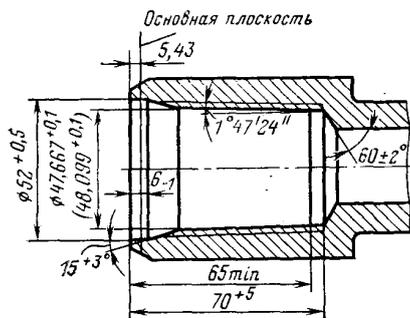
Резьба ниппеля и муфты для соединения с трубой
